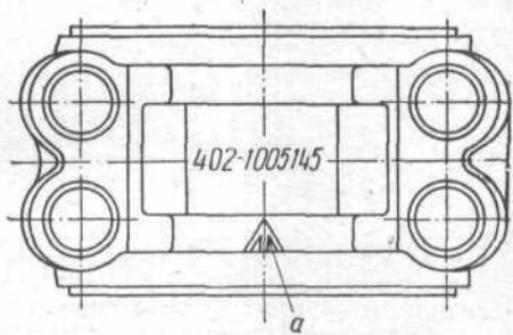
Крышка среднего коренного подшипника коленчатого вала
